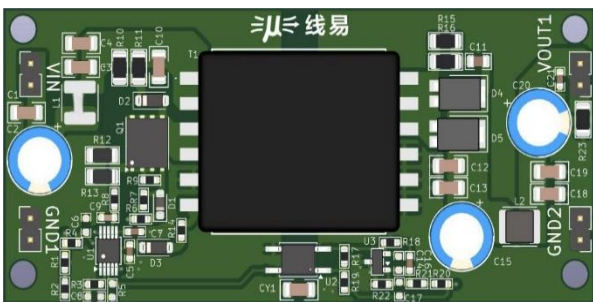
PCB 版图正面 (尺寸: 35x 75mm)
